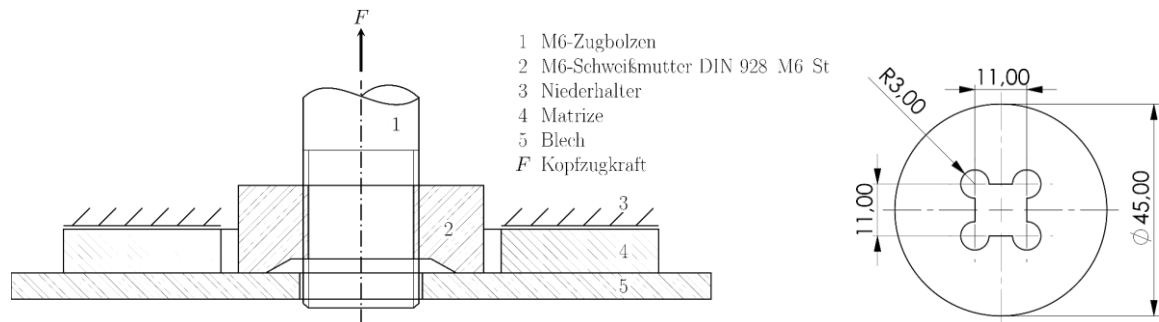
Schematische Darstellung der Vorrichtung für die zerstörende Prüfung der Schweißproben mittels Kopfzugversuch (links) und technische Darstellung der verwendeten Matrizengeometrie für die M6-Vierkantmutter (DIN 928-M6-ST) (rechts)
